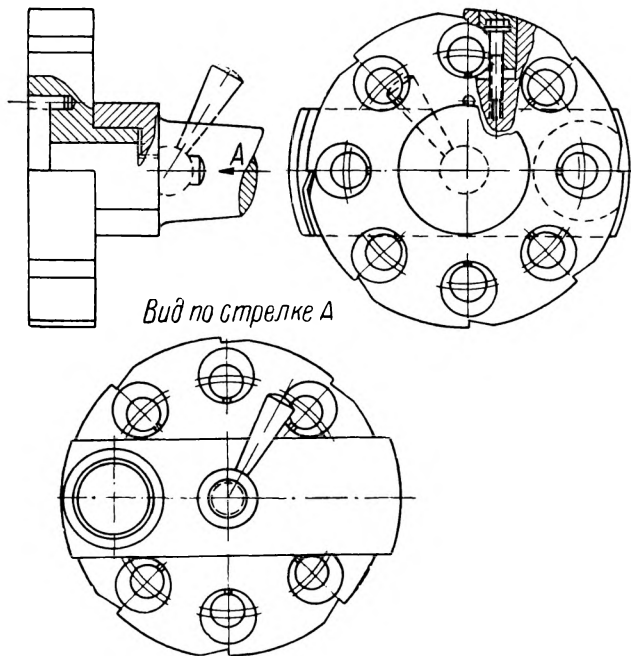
Многорезцовая головка к пиноли задней бабки токарного станка.
